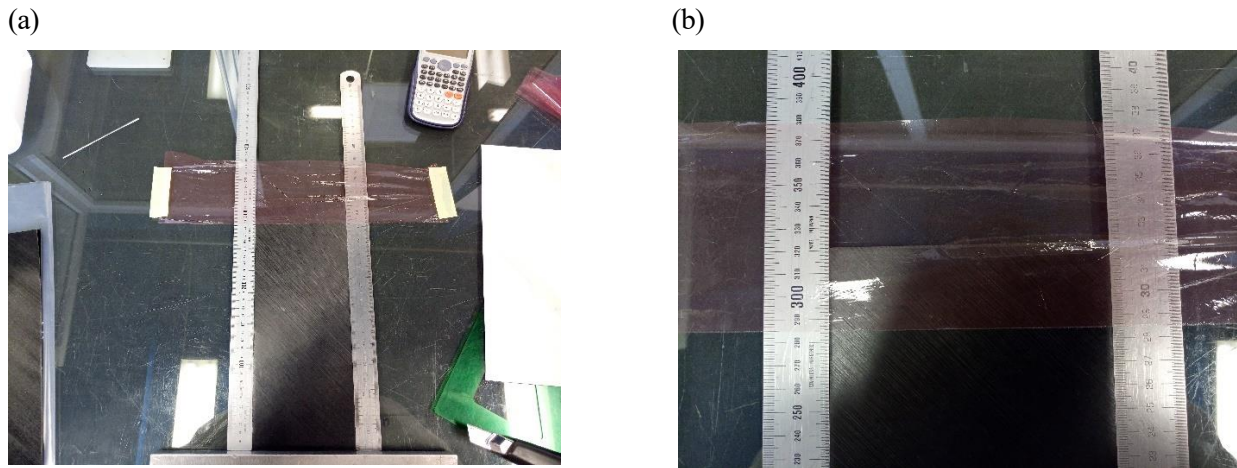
(a) Lámina de desmoldeante del extremo y, (b) Detalle de la longitud del desmoldeante
